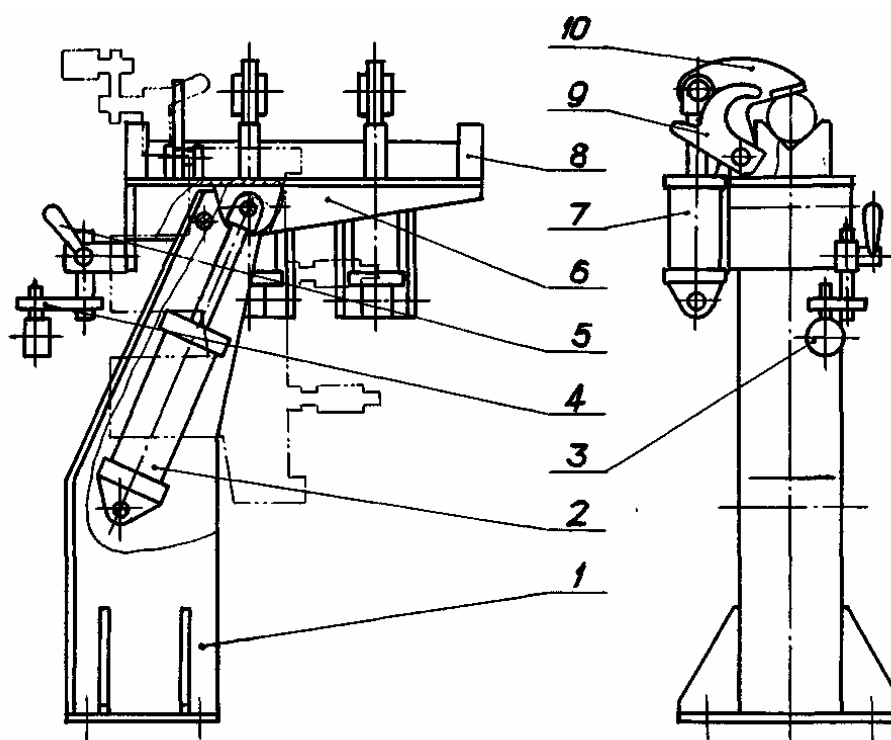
Схема станда для узловой сборки коленчатого вала с маховиком и сцеплением: 1 – корпус; 2 и 7 – пневмоцилиндры; 3 – индикаторная головка; 4 – стойка; 5 – рукоятка; 6 – поворотная рама; 8 – призма; 9 – захват; 10 – рычаг
